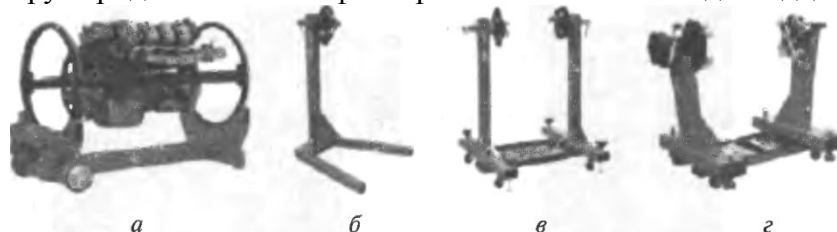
Стенды для разборки/сборки двигателей и коробок передач фирмы RAVAGLIOLY (Италия): а — R 15 — для крупногабаритных силовых агрегатов; б — R 10 — одностоечный с креплением агрегата по фланцу; в — R 12 — двухстоечный передвижной; г — R 11 — двухстоечный с электромеханическим приводом поворота изделия
